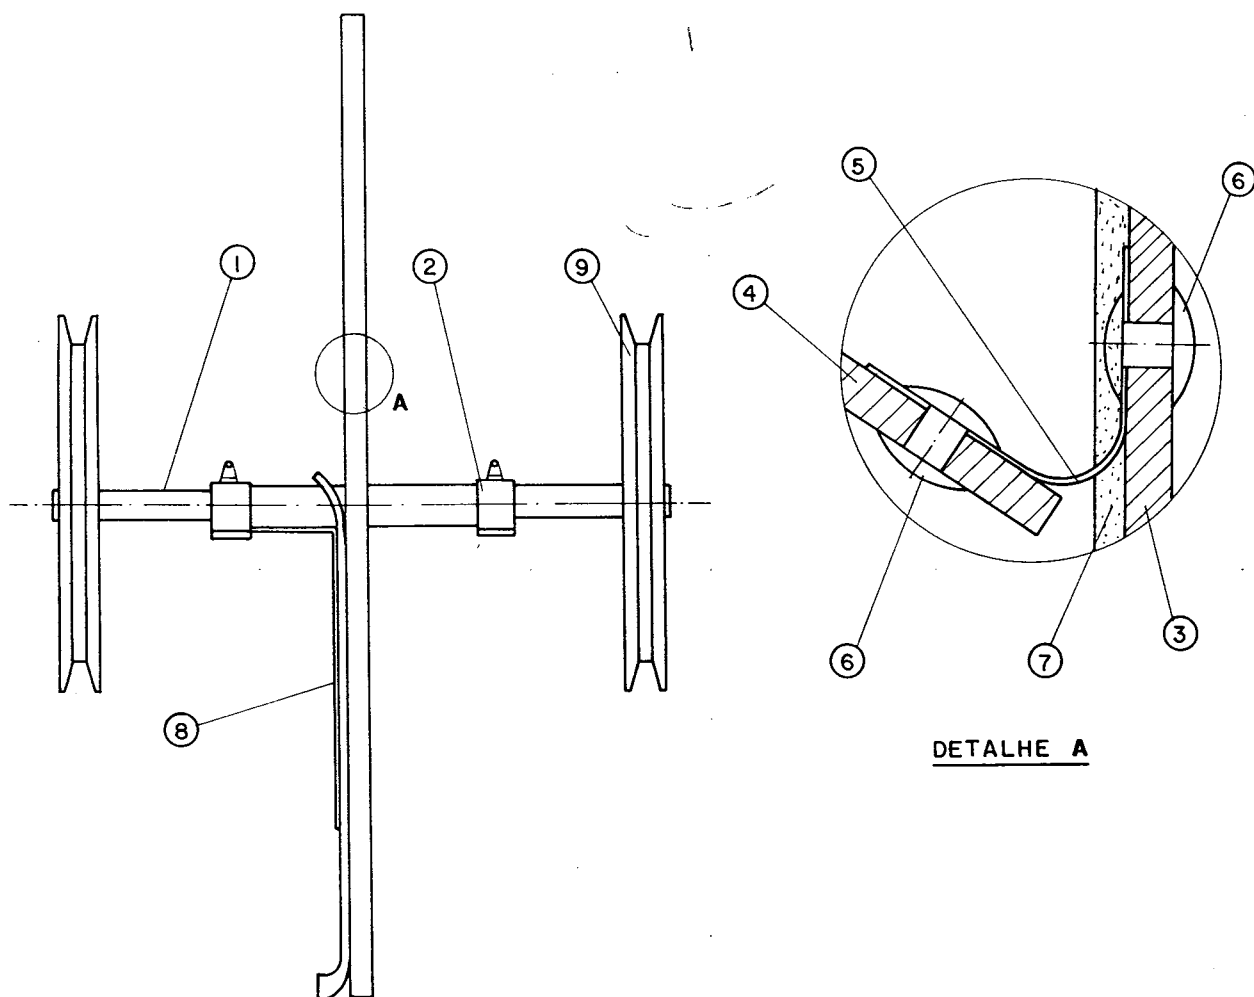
Vista frontal do conjunto plantador com um detalhe do posicionamento das plaquetas.
